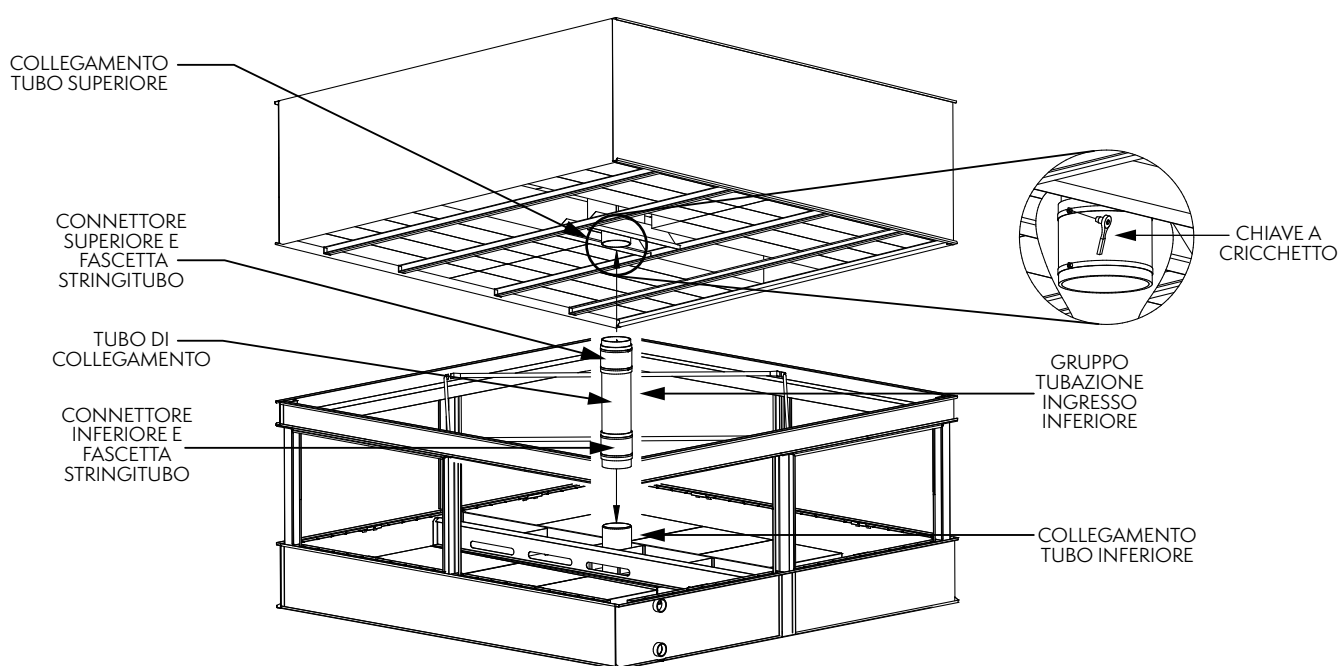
Installazione del tubo montante sull'ingresso inferiore
